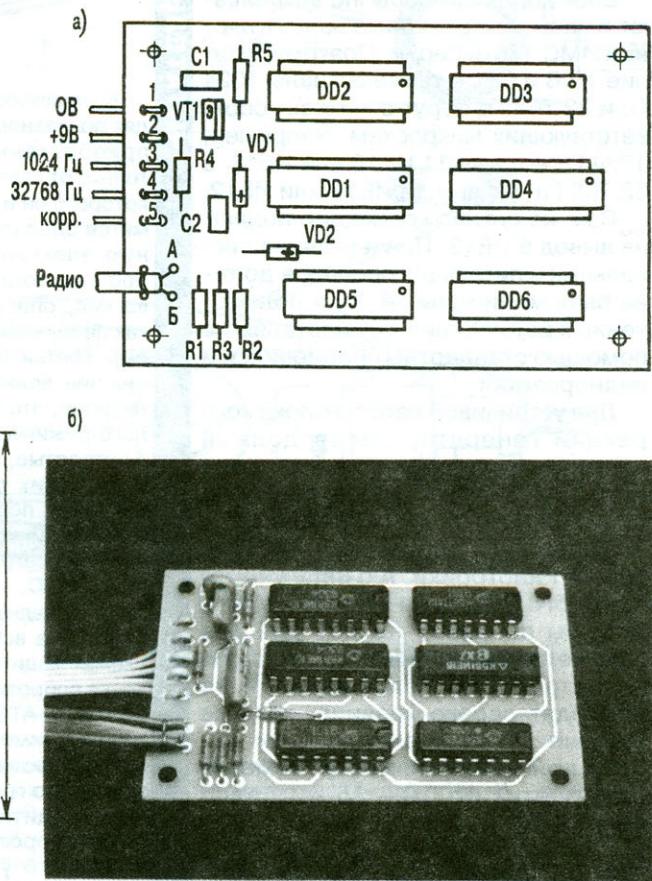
Сборочный чертеж (а) и готовый блок коррекции (б).
